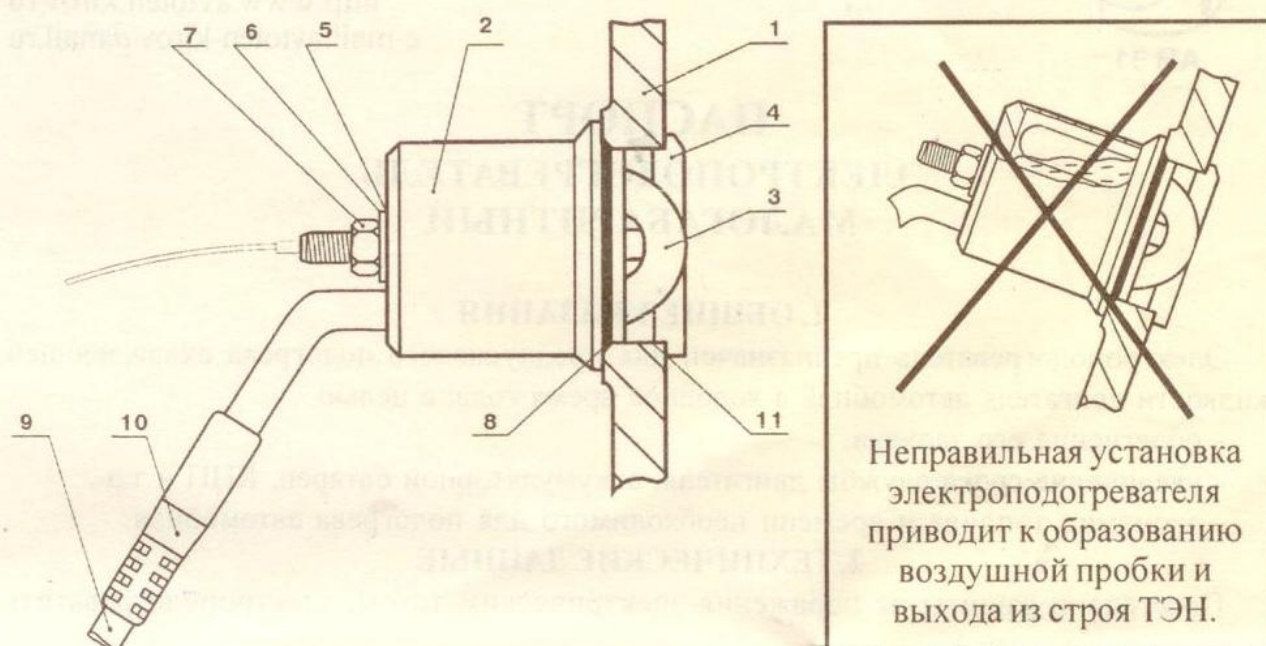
1-стенка блока цилиндров; 2 - корпус электроподогревателя; 3 - ТЭН; 4 - прижим; 5 - резиновая уплотнительная шайба; 6 - шайба; 7 - гайка; 8 - кольцо уплотнительное; 9 - шнур армированный; 10 - колодка соединительная; 11 - посадочное место.
